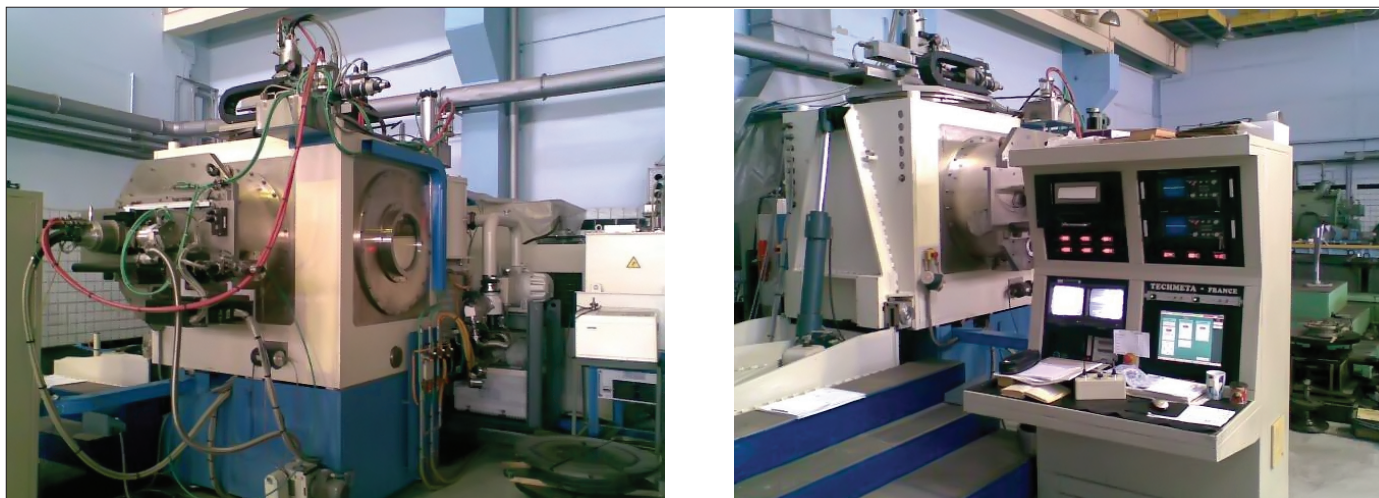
Внешний вид установки для сварки и лучевой термообработки Lara-52
